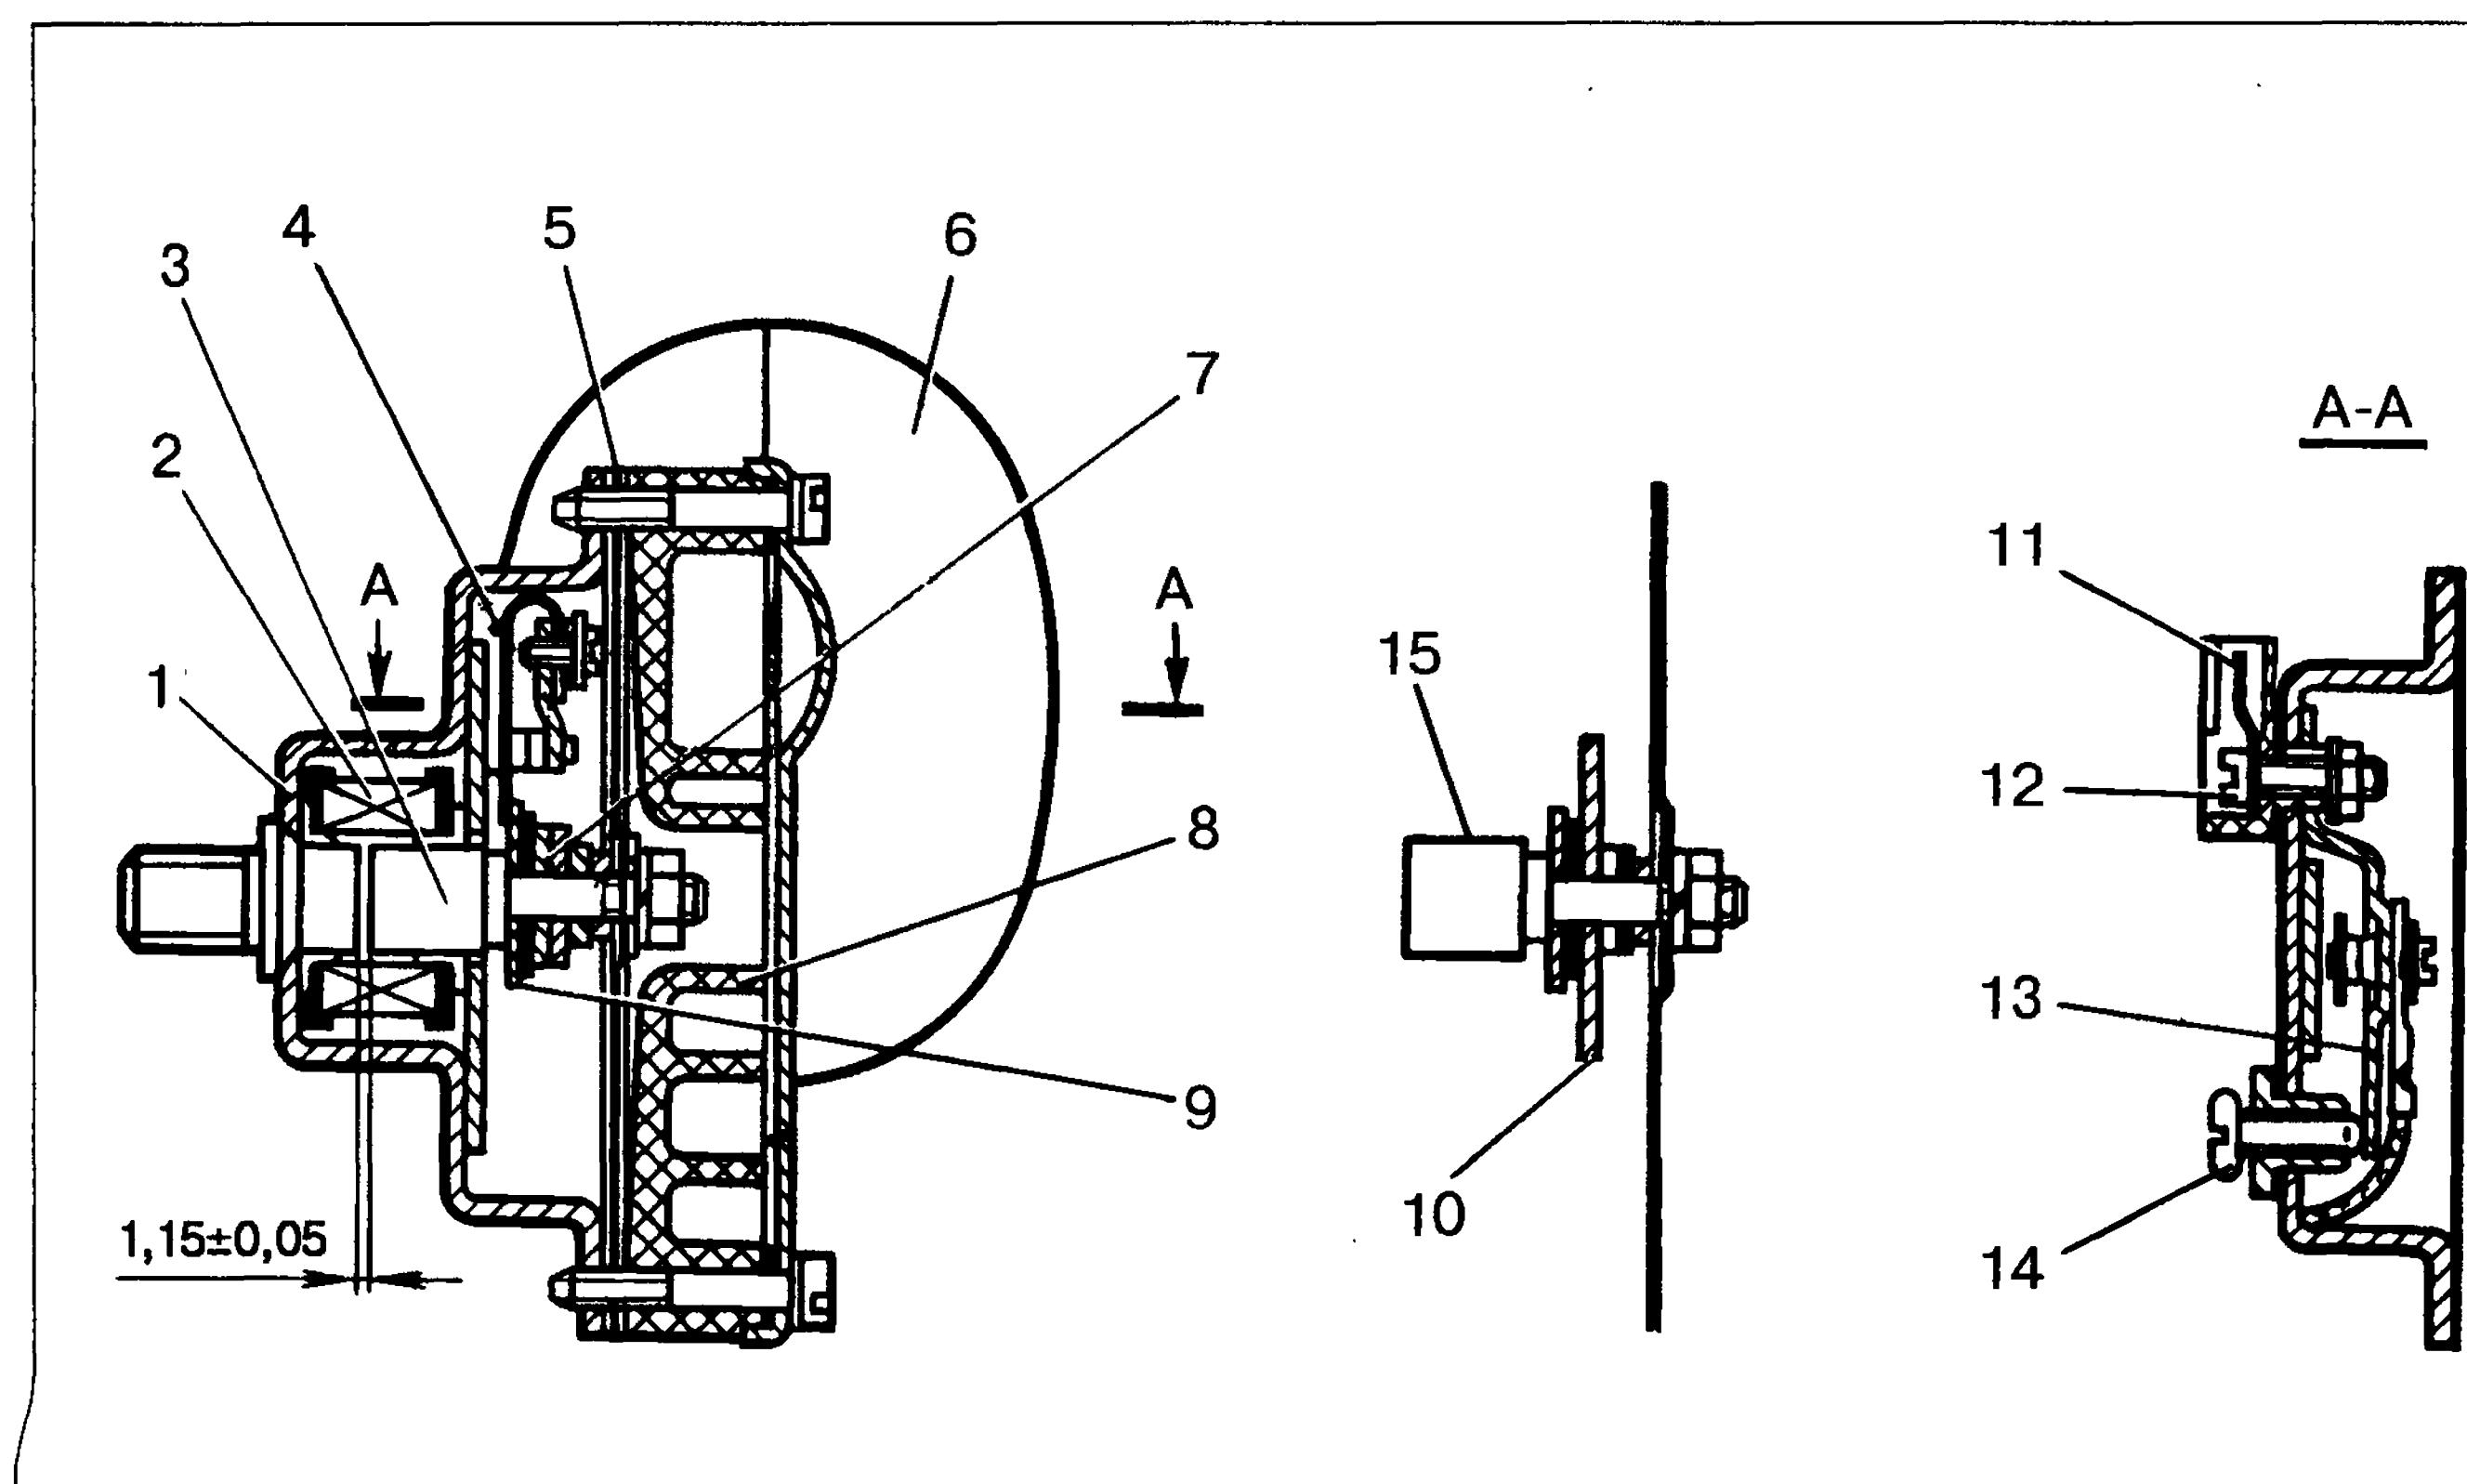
Звуковой сигнал: 1-корпус; 2-обмотка сердечника; 3-якорь; 4-упругая пластина; 5-мембрана; 6-крышка диффузора; 7-груз; 8-корпус диффузора; 9-шайба; 10-груз; 11-штекер; 12-винт; 13-держатель; 14-регулирующий винт; 15-якорь с мембраной сигнала высокого тона
